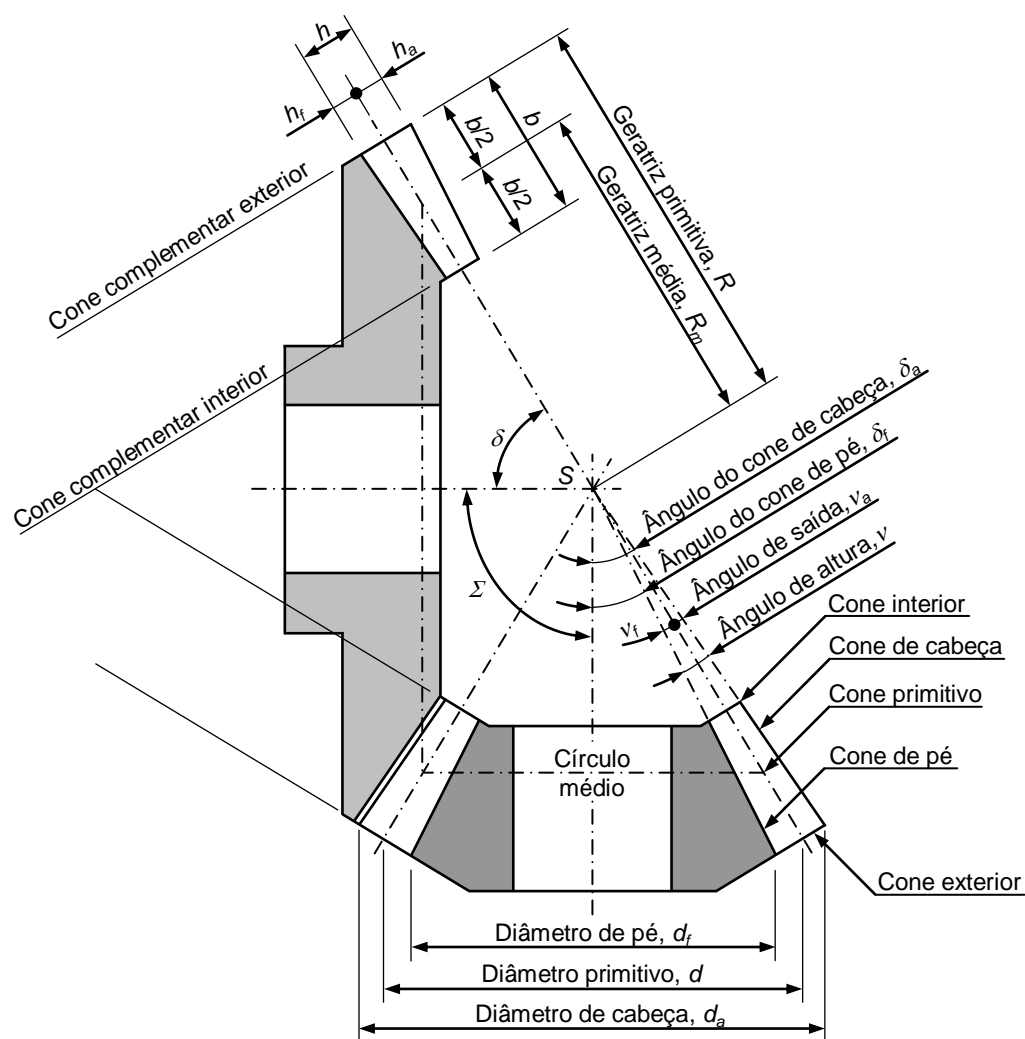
Nomenclatura fundamental de uma engrenagem cónica.
